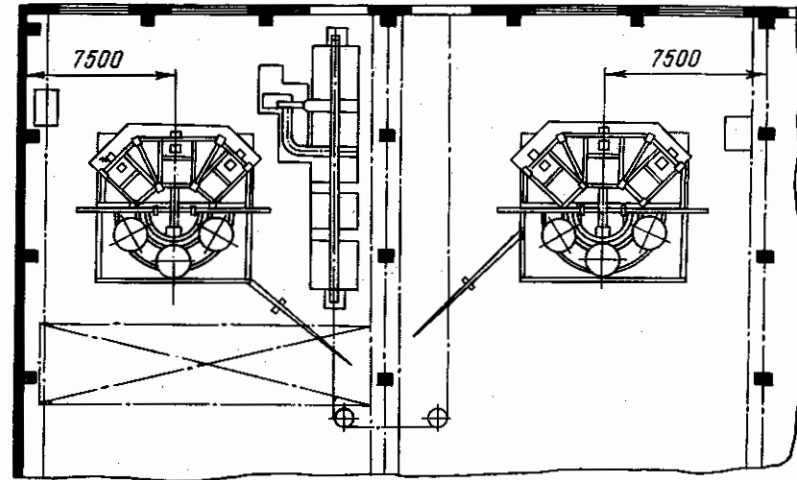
Планировка участка гидроочистки отливок с установками непрерывного действия роторного типа
